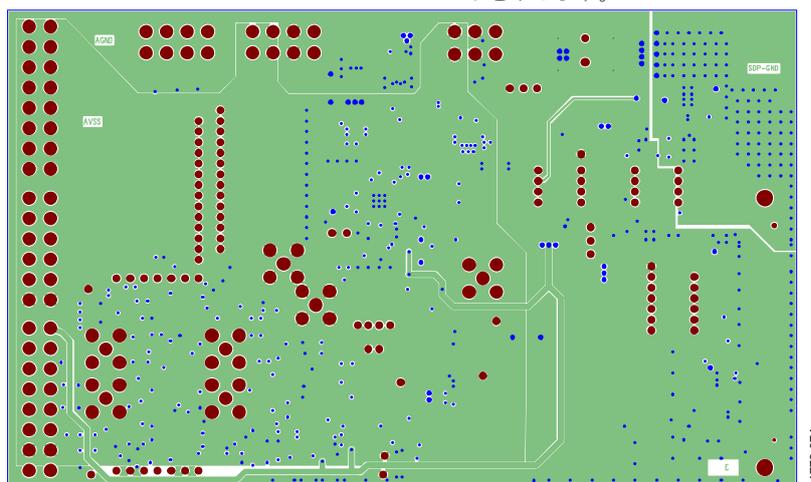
EVAL-AD7173-8SDZ の PCB 第 3 層
